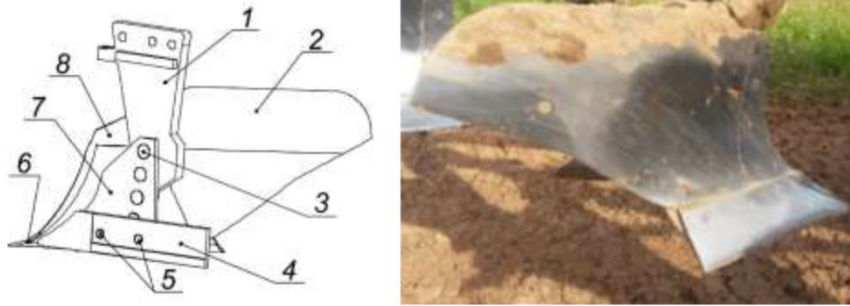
Корпус: 1 – стійка; 2 – крило відвалу; 3 – болт; 4 – дошка польова; 5 – болт із шайбою та гайкою; 6 – леміш; 7 – башмак; 8 – груди відвалу.
